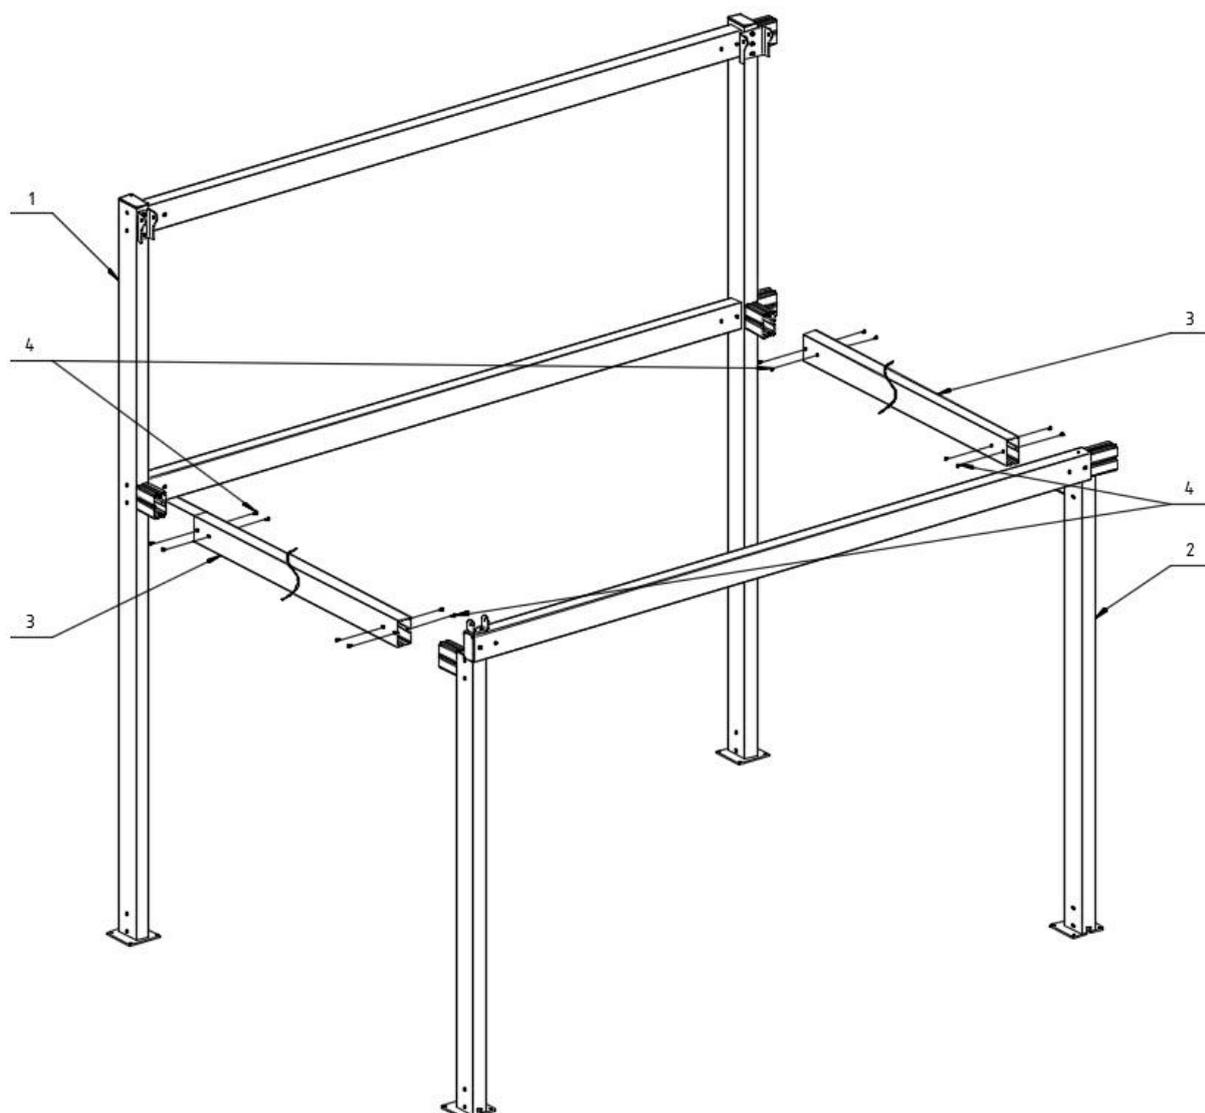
Méthode d'assemblage des poutres latérales dans le premier module : 1 - Module du poteau haut, 2 - Module du poteau bas, 3 Poutre latérale, 4 - Vis M8x16.
